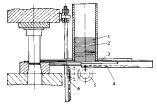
齿轮齿条传动闸门式送料机构 1—工件: 2—料匣: 3—推板: 4、6—齿条: 5—齿轮
